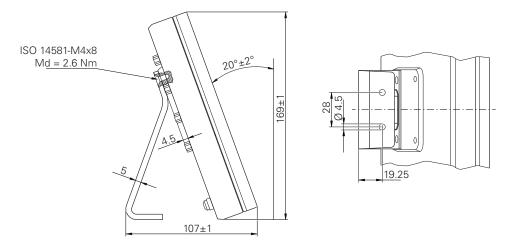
Dimensões do aparelho com pé de suporte Single-Pos
